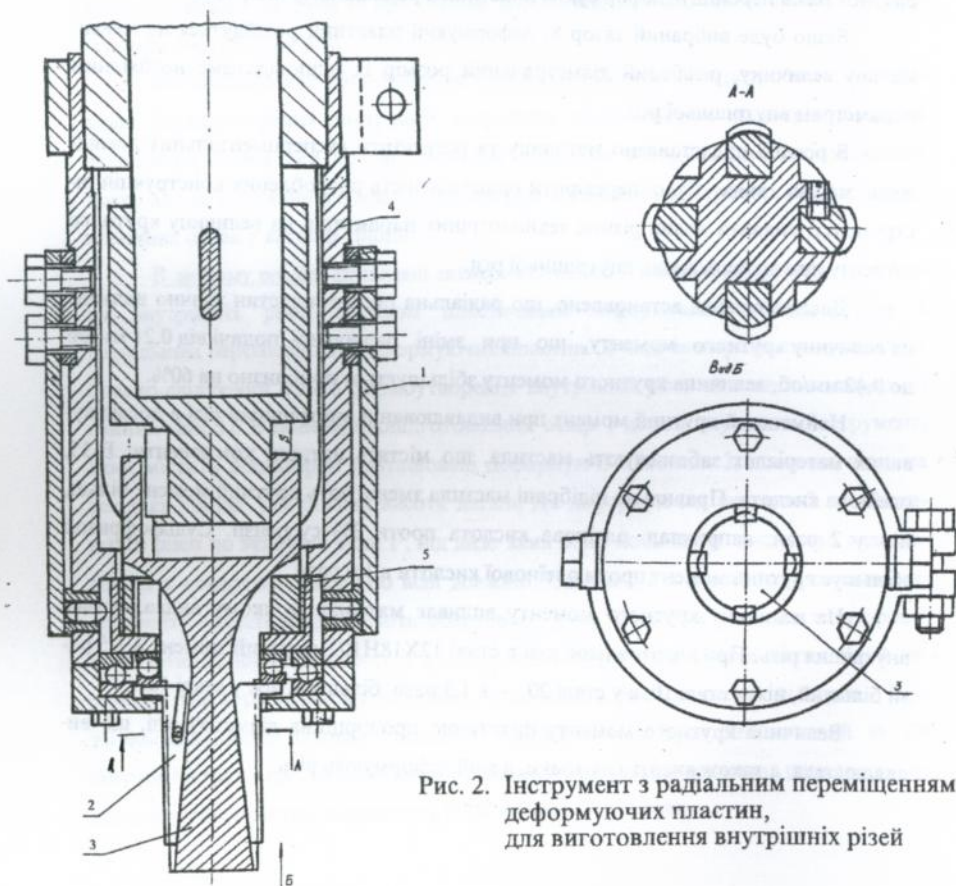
Інструмент з радіальним переміщенням деформуючих пластин, для виготовлення внутрішніх різей
